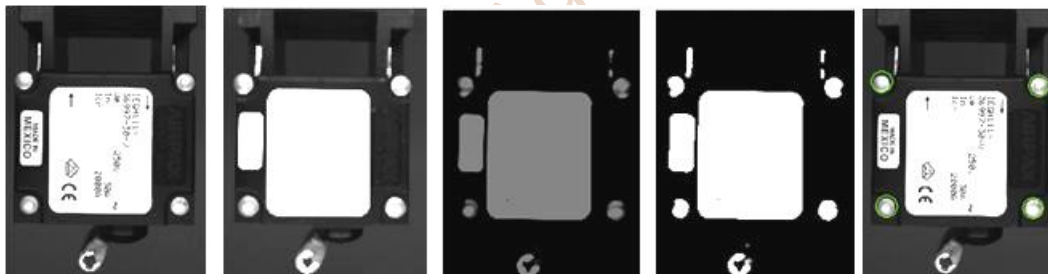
Secuencia de imágenes en inspección cara frontal de remaches.
